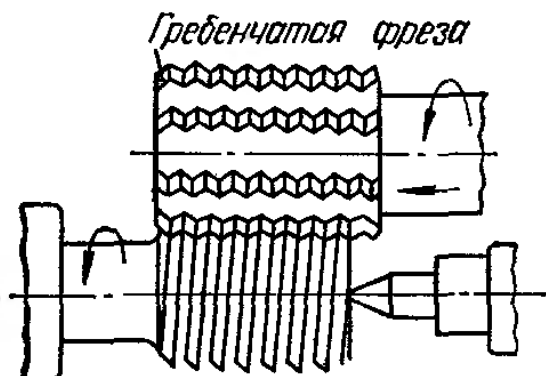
Схема нарезания резьбы гребенчатой фрезой
